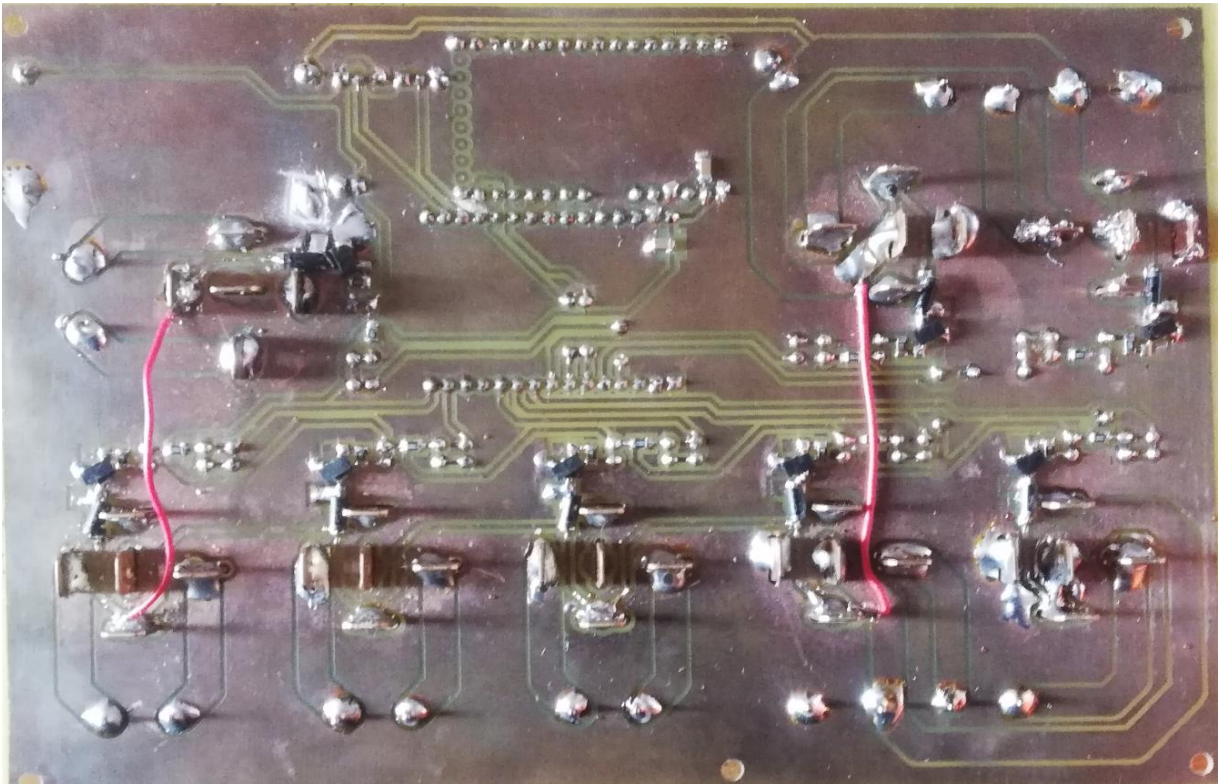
Soldadura de los componentes en el circuito diseñado. Fuente: Propia
